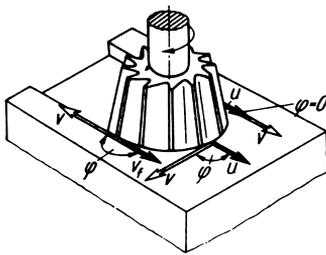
Vorschubrichtungswinkel φ beim Fräsen mit Stirnfräser (nach DIN 6580)
